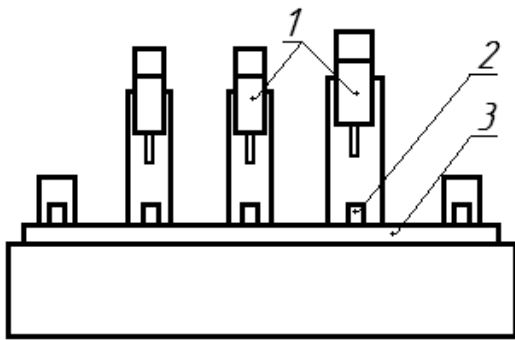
Компоновка агрегатных станков с прямолинейным перемещением заготовок
